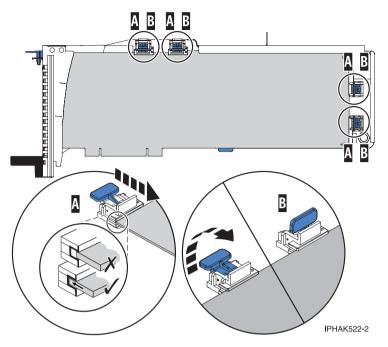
Langen PCIe-Adapter in PCIe-Adapterkassette installieren
